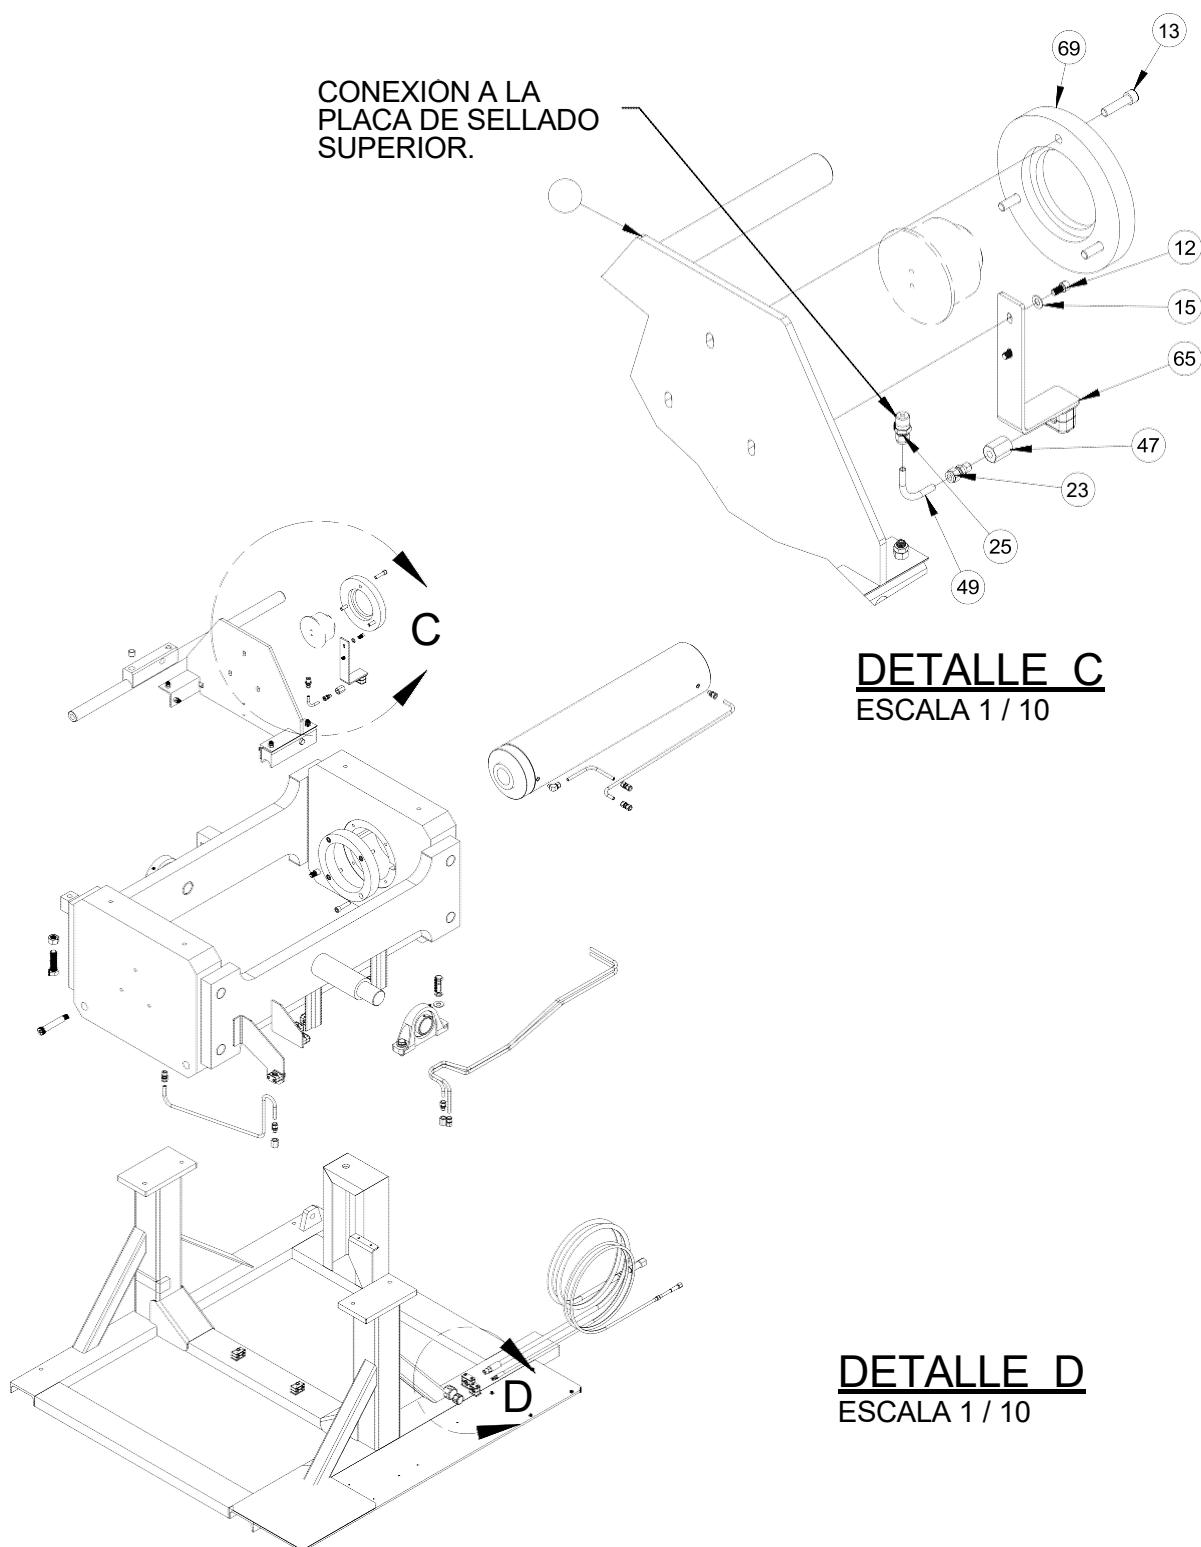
USV-16-200T MONTAJE DETALLE C Y D 1 (P/N 91593)
